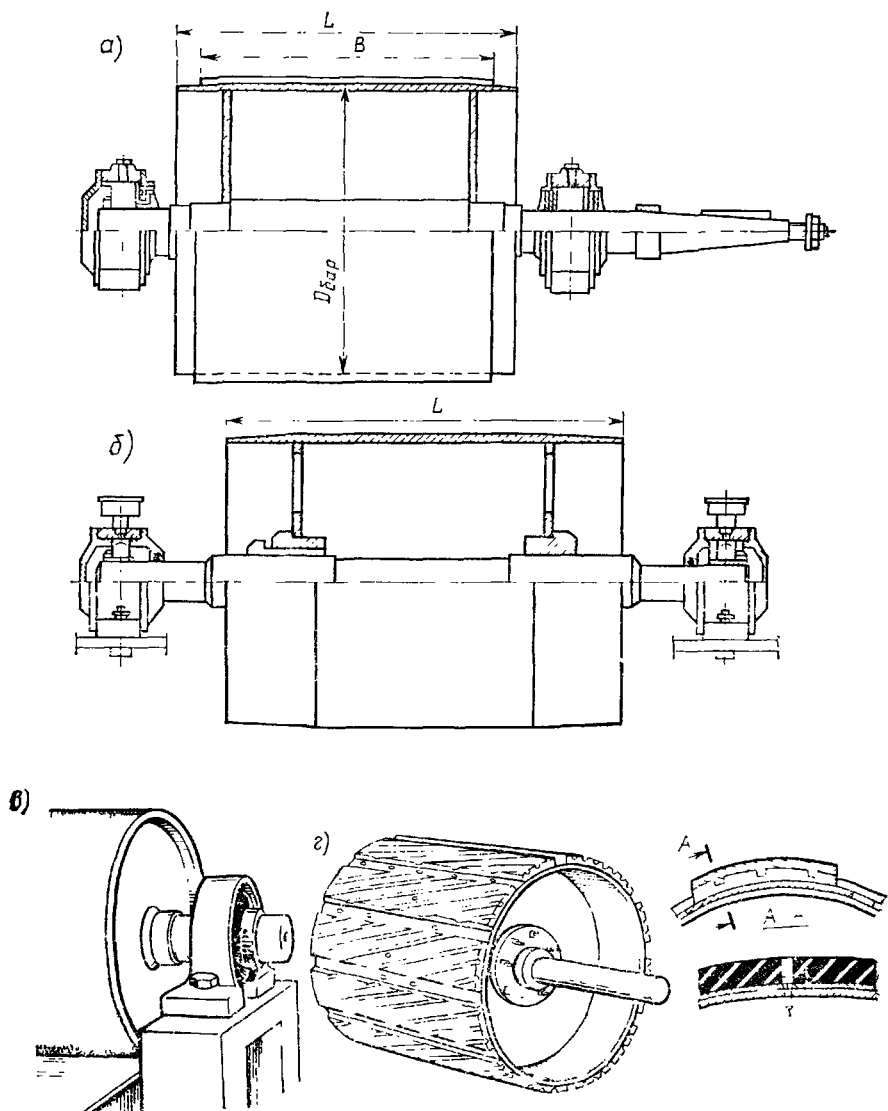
Барабаны для конвейера с резиноканавчатой лентой
